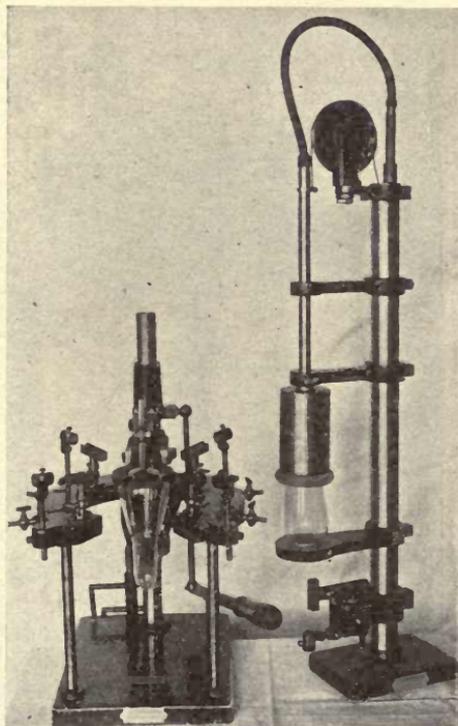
Kolbenabzieh- und Stengelansetzmaschine.
